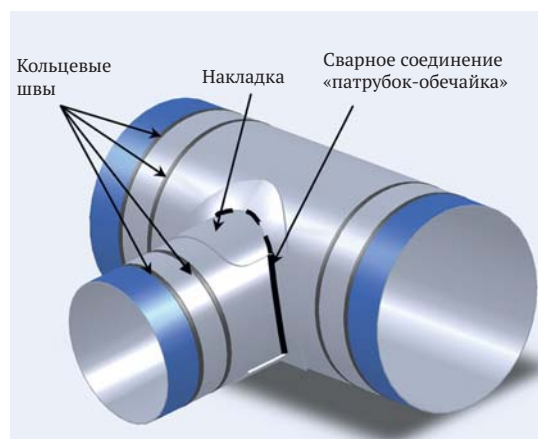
Эскиз типового сварного тройника с усиливающей накладкой
